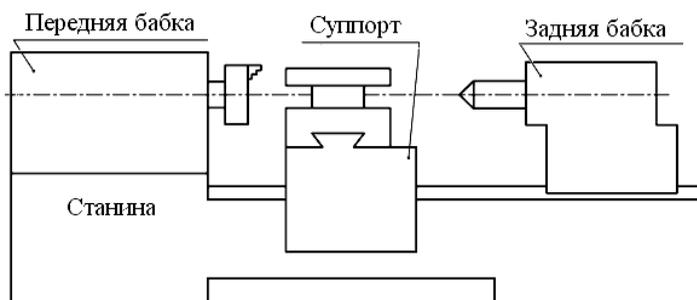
Типовые базовые детали и упрощенная компоновка токарного станка
